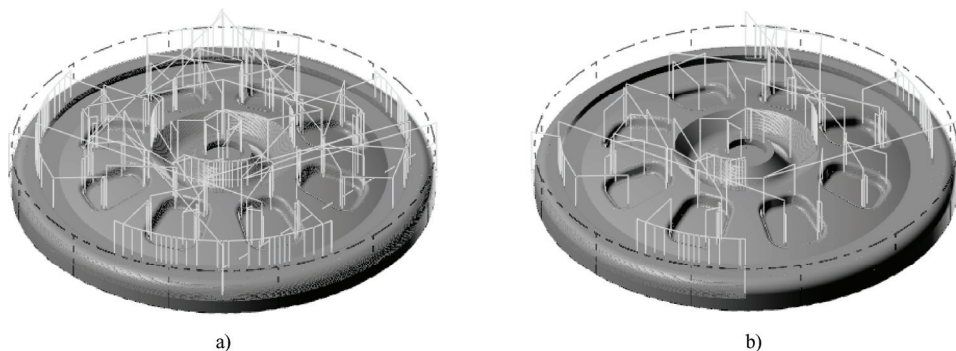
产生平行陡斜面精加工 2 的刀具路径
